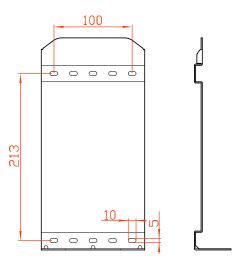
Dimens ces da instala ção otimizada (unidade: mm)
